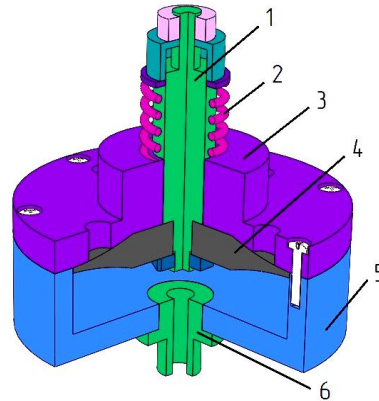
Конструкція зворотного клапана для модуля очистки забруднень потоком твердих частинок: 1 – шток; 2 – пружина; 3 – кришка; 4 – гумовий пелюстковий клапан; 5 – корпус; 6 – штуцер
